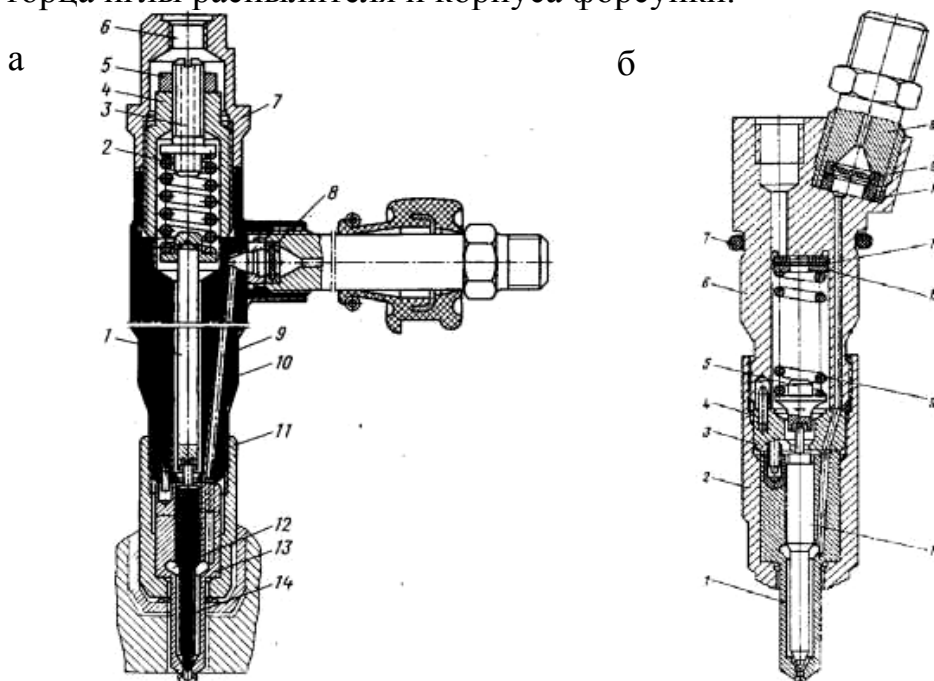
Устройство форсунок двигателей ЯМЗ-236 (238) (а) и КамАЗ 740 (б):
